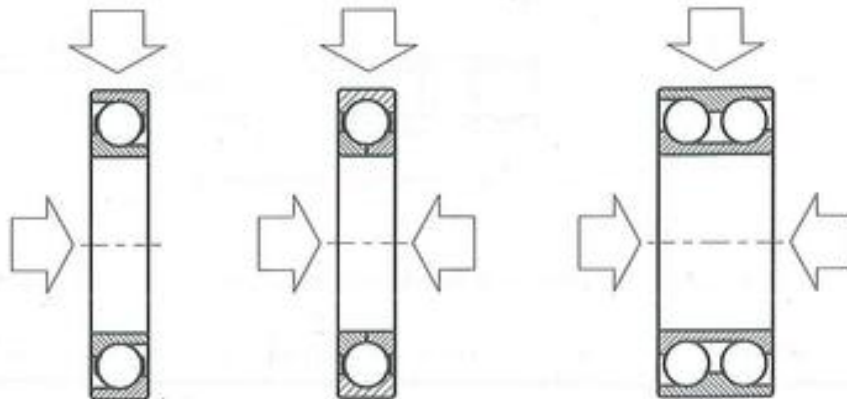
Rodamientos de bolas con contacto angular.
